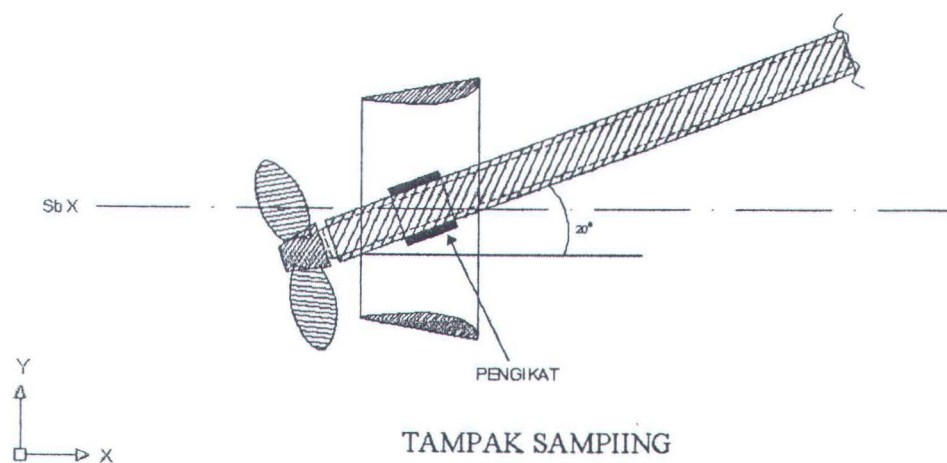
Posisi 1 adjustable circulating duct terpasang searah poros propeller
